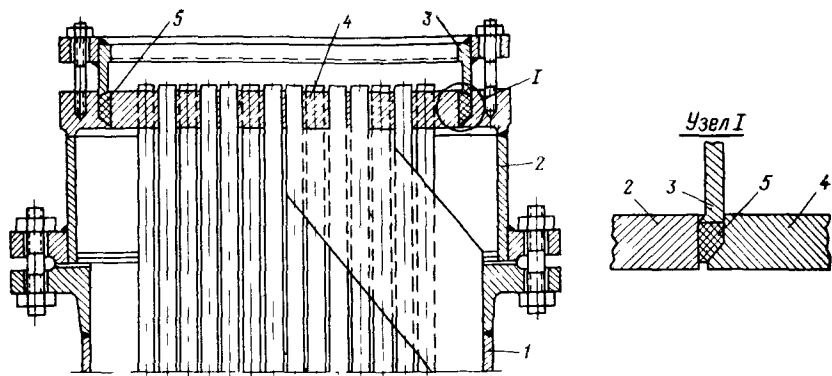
Приспособление для опрессовки теплообменников с плавающей головкой
